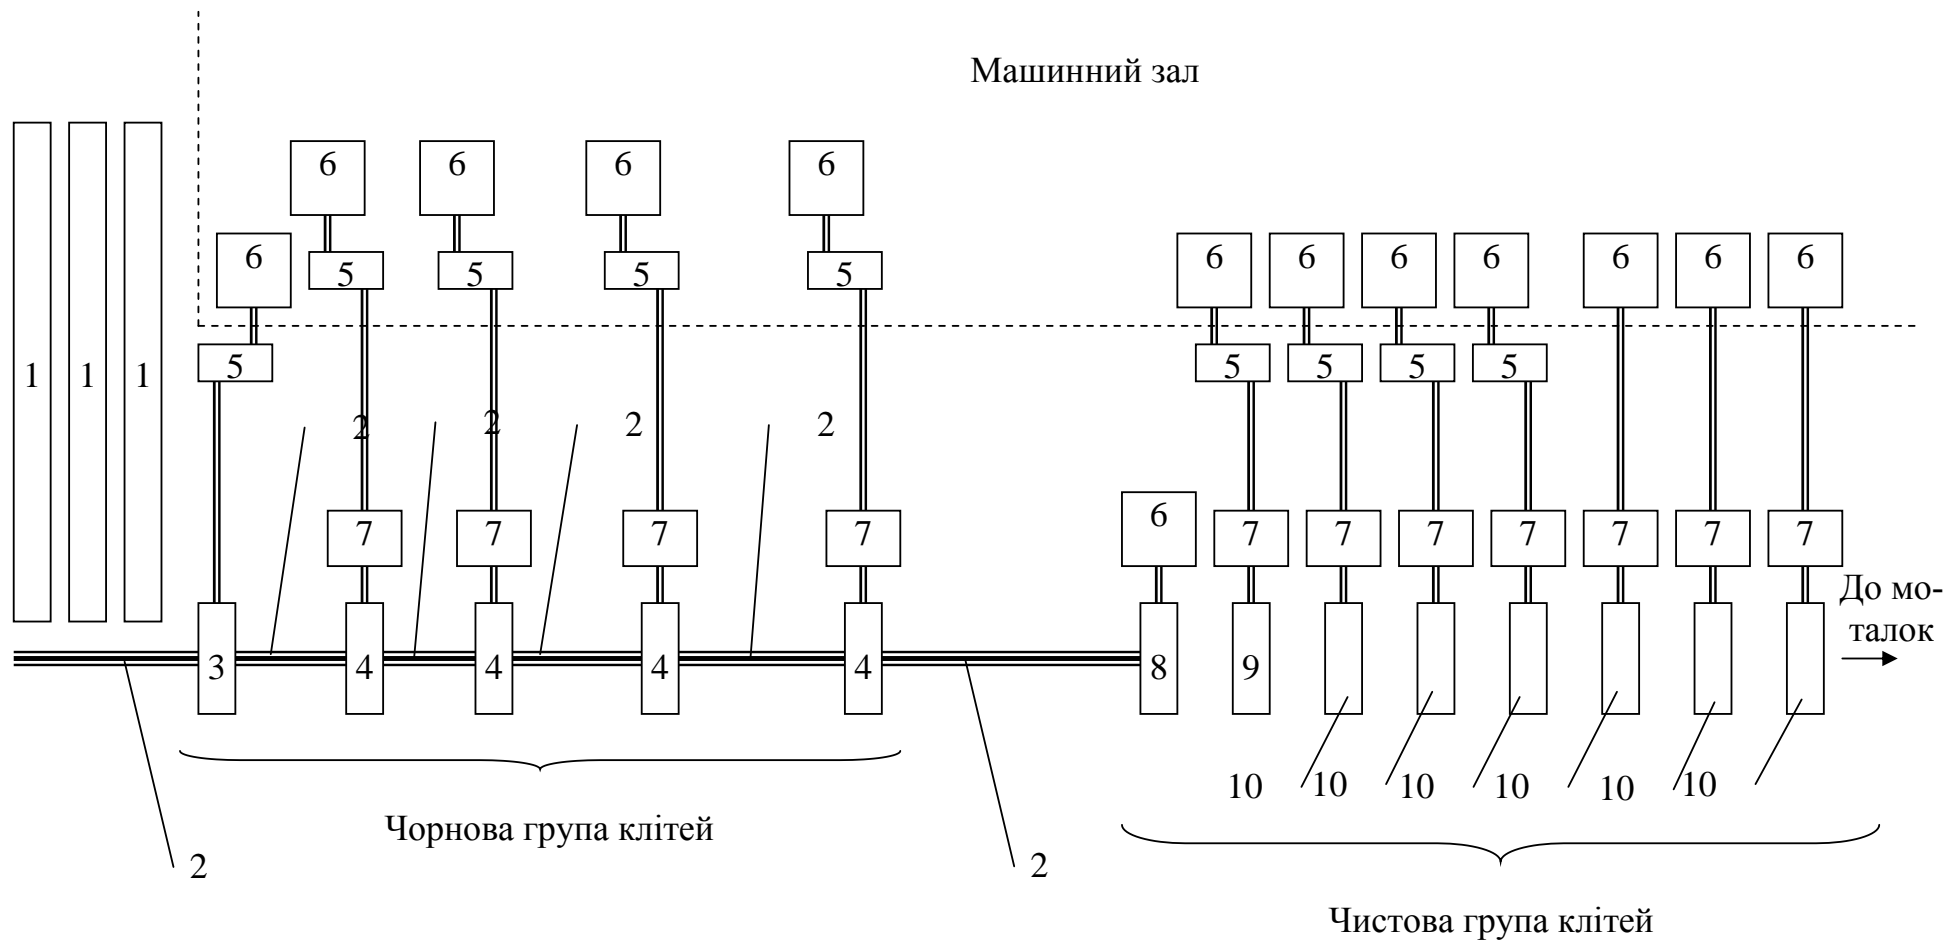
Схема розташування обладнання неперервного широкосмугового стана гарячої прокатки
